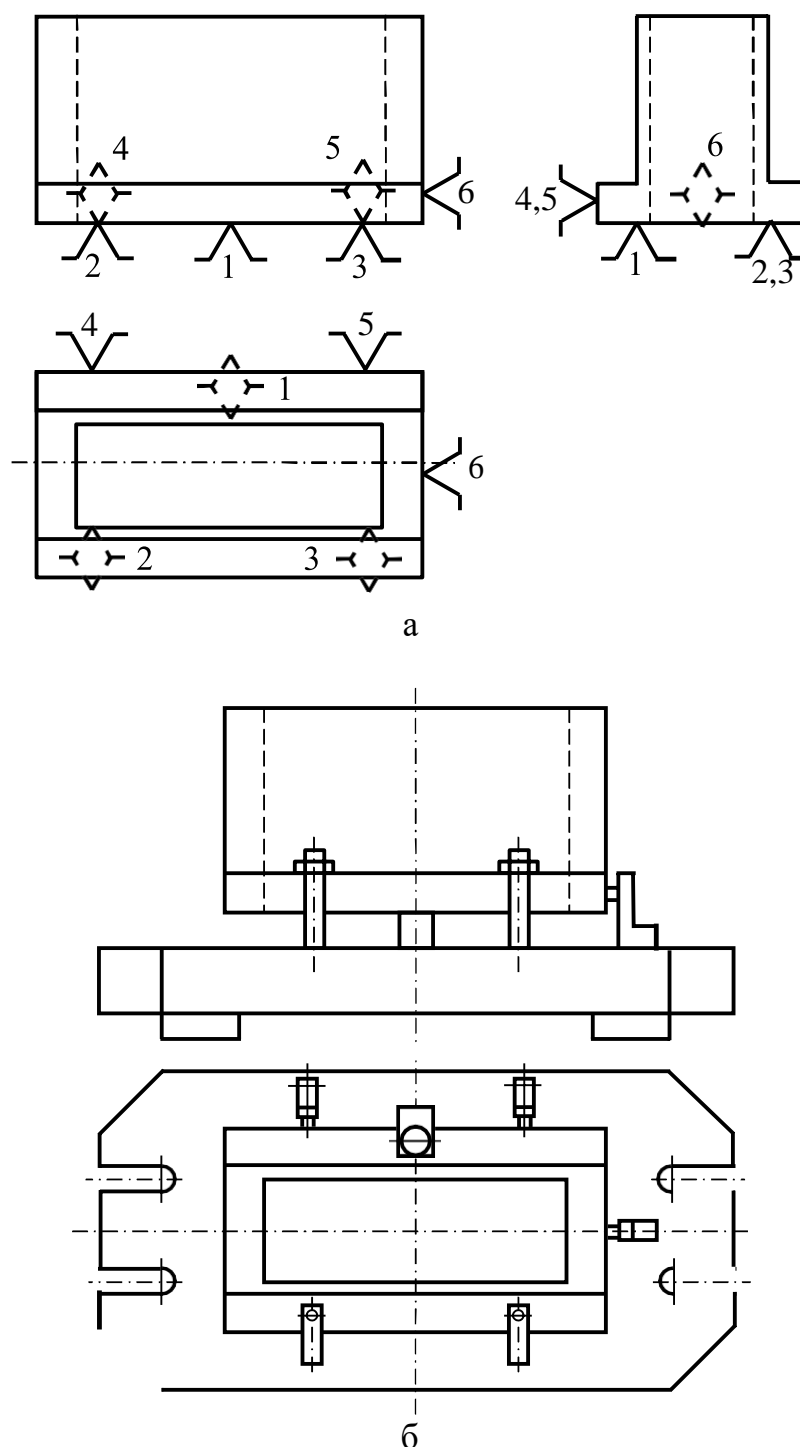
Схемы базирования (а) и установки (б) детали в координатный угол
